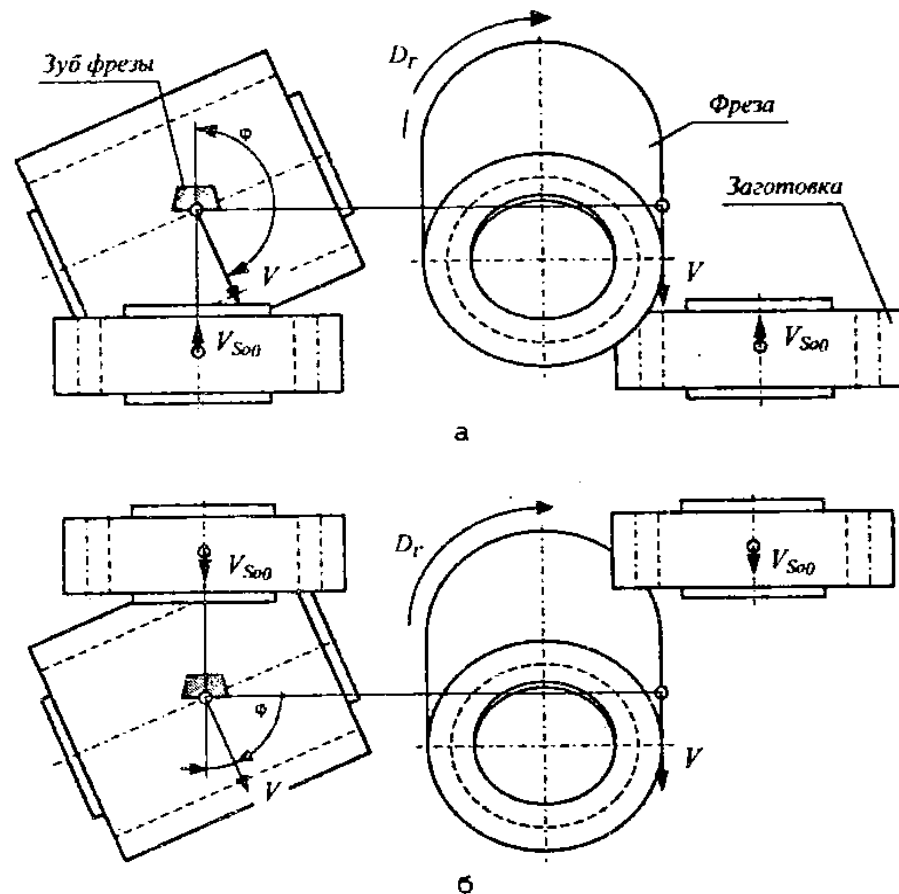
Схема роботи червяної зуборізної фрези
